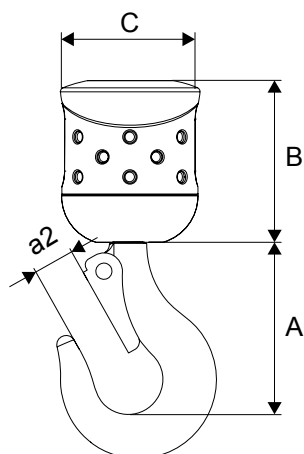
Dimensions du moufle à chute unique, SL05-SL10
